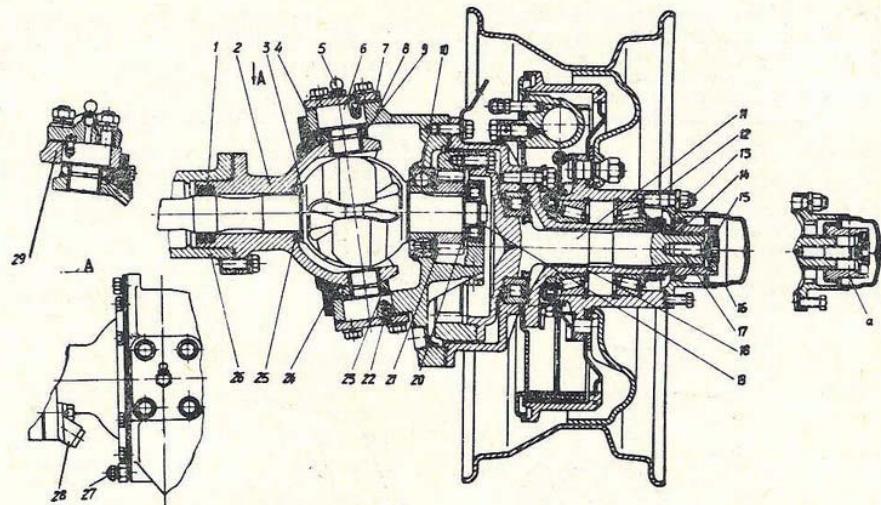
Ložisko redukce v kolech, uložené v pouzdru
